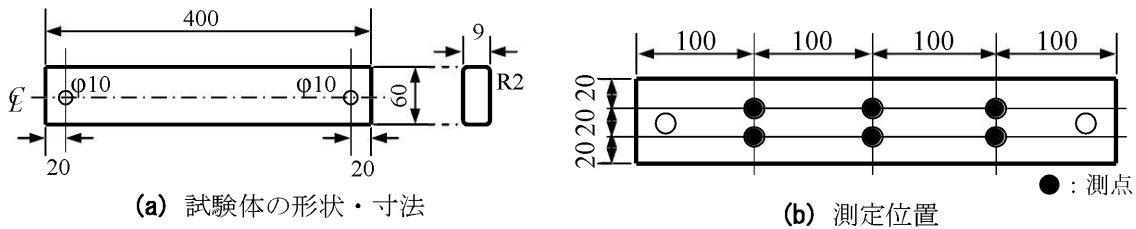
試験体の形状・寸法および測定位置 (単位 : mm)
